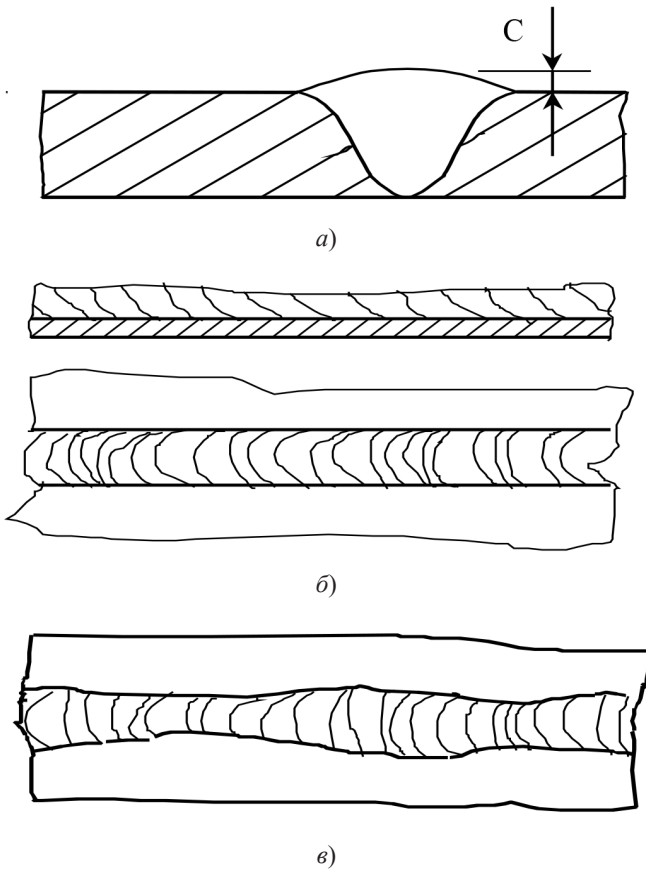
Дефекты сварных соединений: а – усиление шва; б – грубая чешуйчатость; в – неравномерная ширина шва
